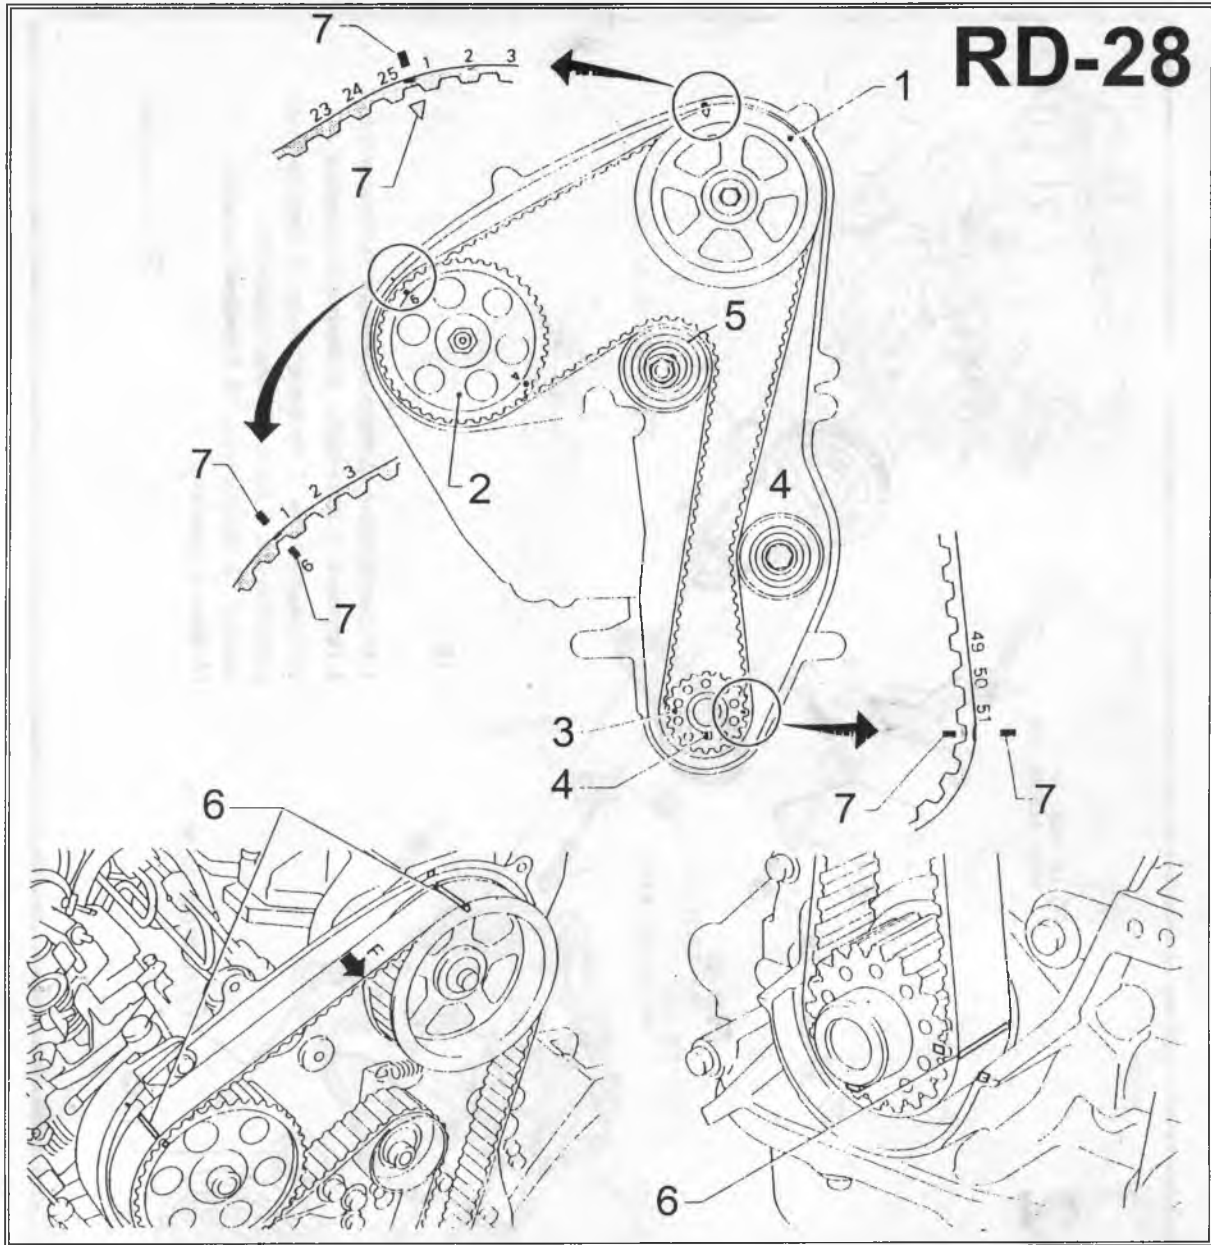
1. Зубчатый шкив распределительного вала. 2. Зубчатый шкив ТИВД. 3. Зубчатый шкив коленчатого вала. 4. Опорный ролик. 5. Натяжной ролик. 6. Белые линии. 7. Метки совмещения. 8. Шпоночная канавка на коленчатом валу.
